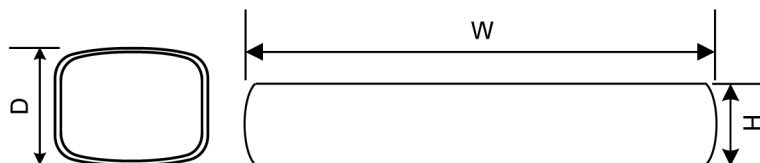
Skjematisk fremstilling, mål i millimeter
